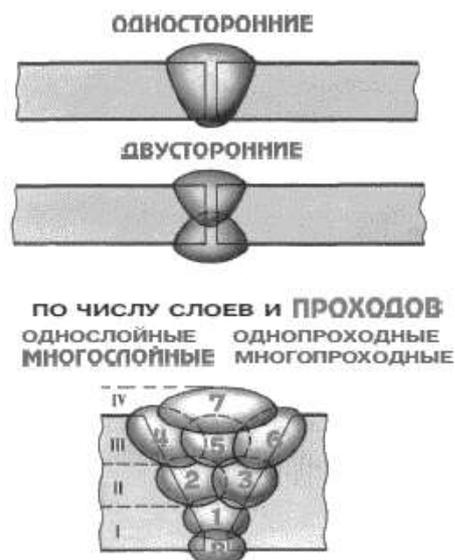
Виды сварных соединений по способу выполнения
